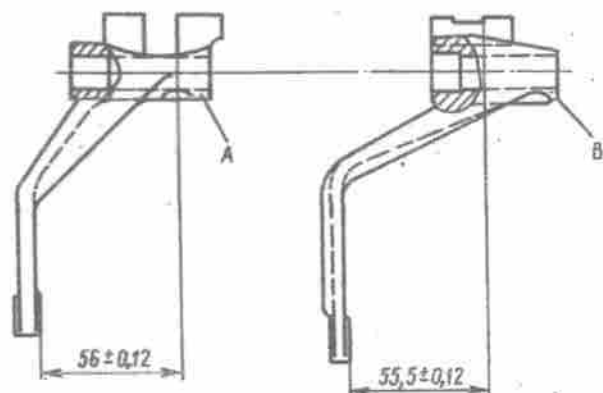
Kontrollmaße der Schaltgabeln des Wech-selgetriebes:
